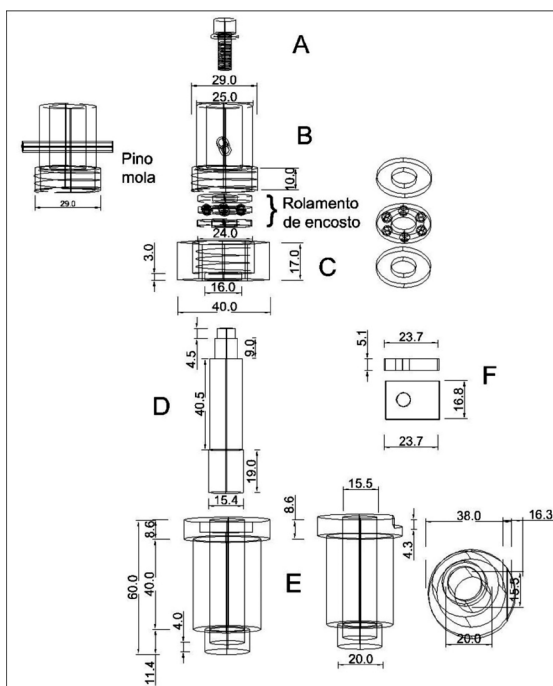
S. Detalhes da construção do conjunto êmbolo (D)/cilindro de molde (E)
